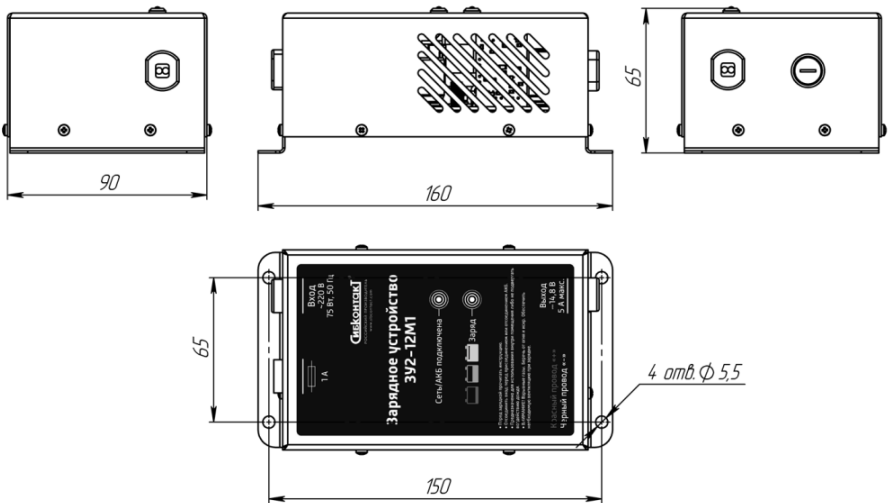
Установочные и габаритные размеры зарядного устройства
